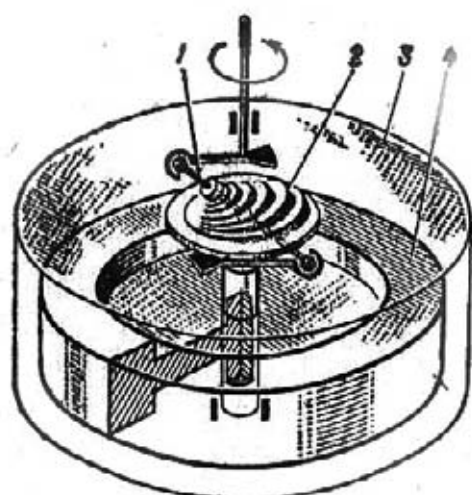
Передача вращения через герметичный корпус поводковой муфтой
